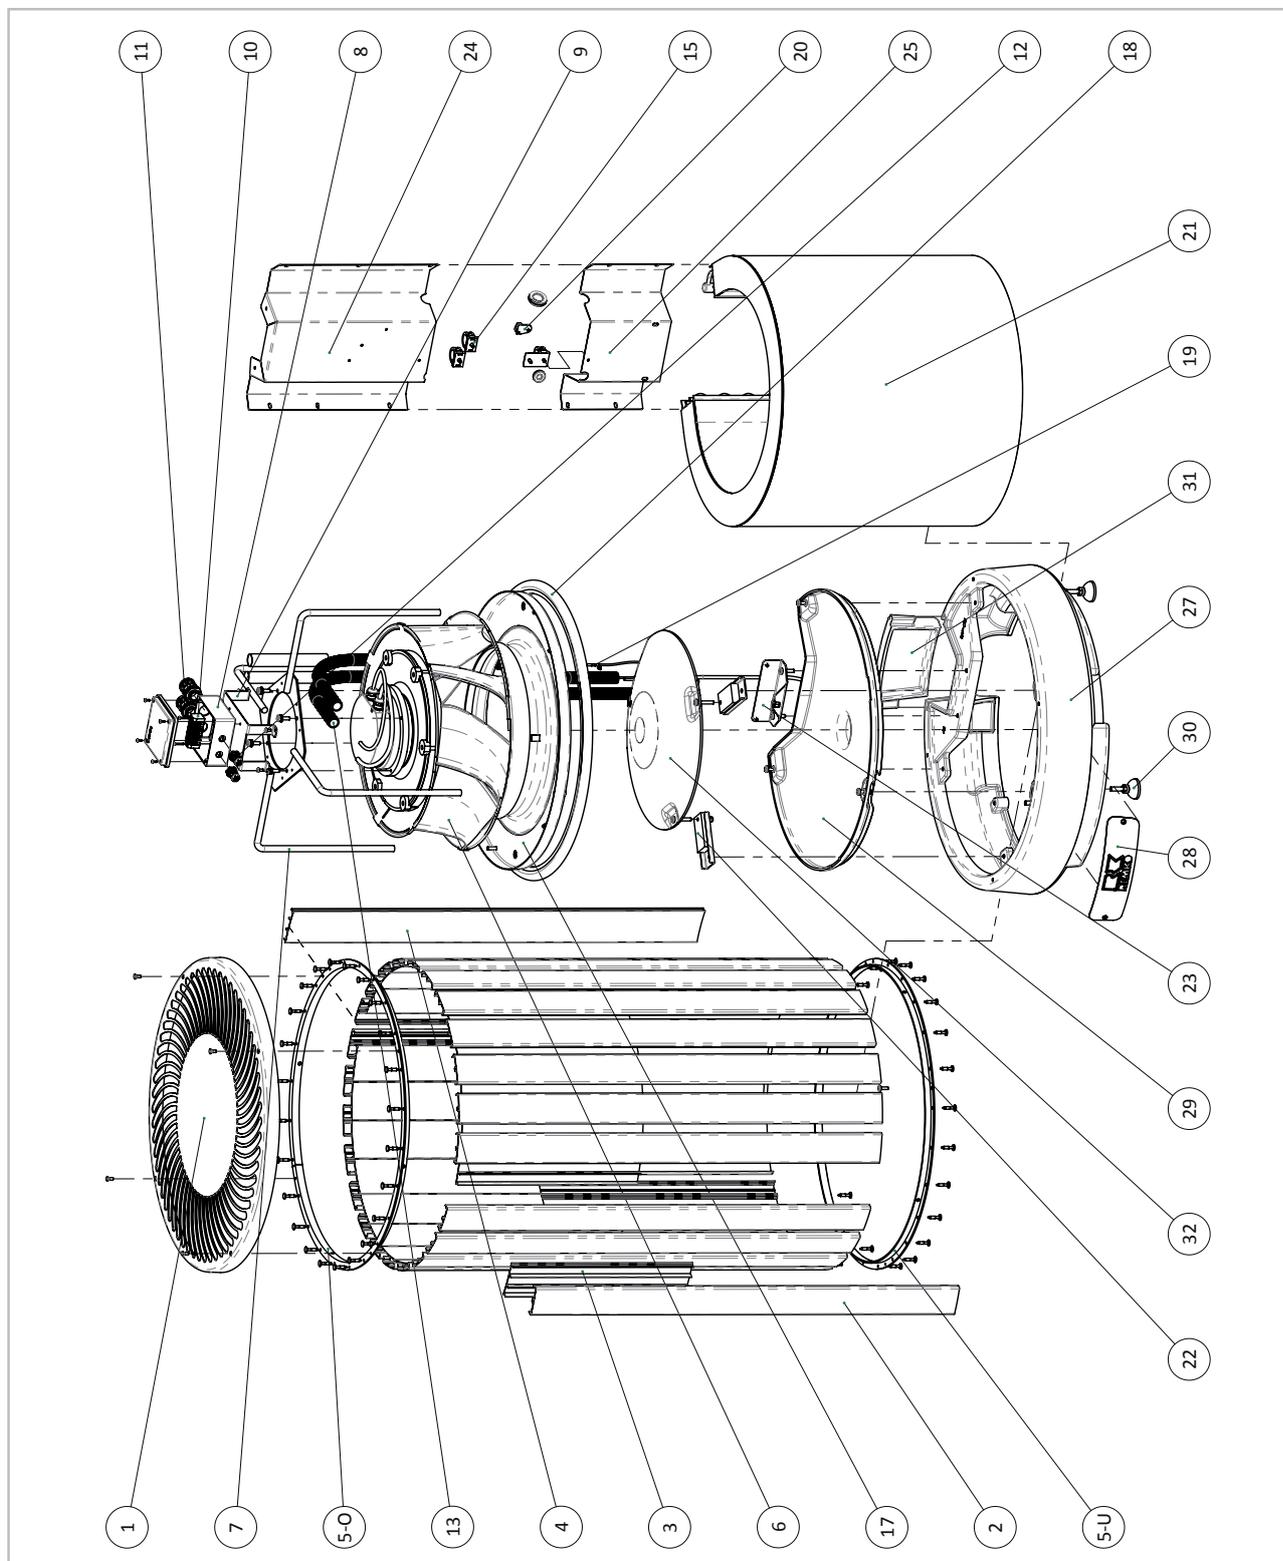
Vue éclatée du module extérieur HTS 80/90/110/130/200/260
